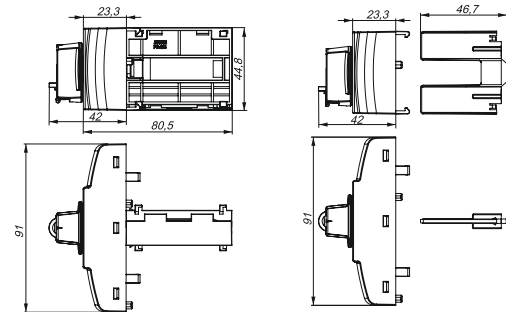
Габаритные и установочные размеры контактов дополнительных / Figure 5 – Overall and mounting dimensions of auxiliary contacts
